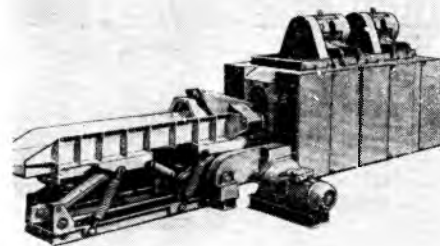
Двухроторный окорочно-зачистной станок 20К40-1
